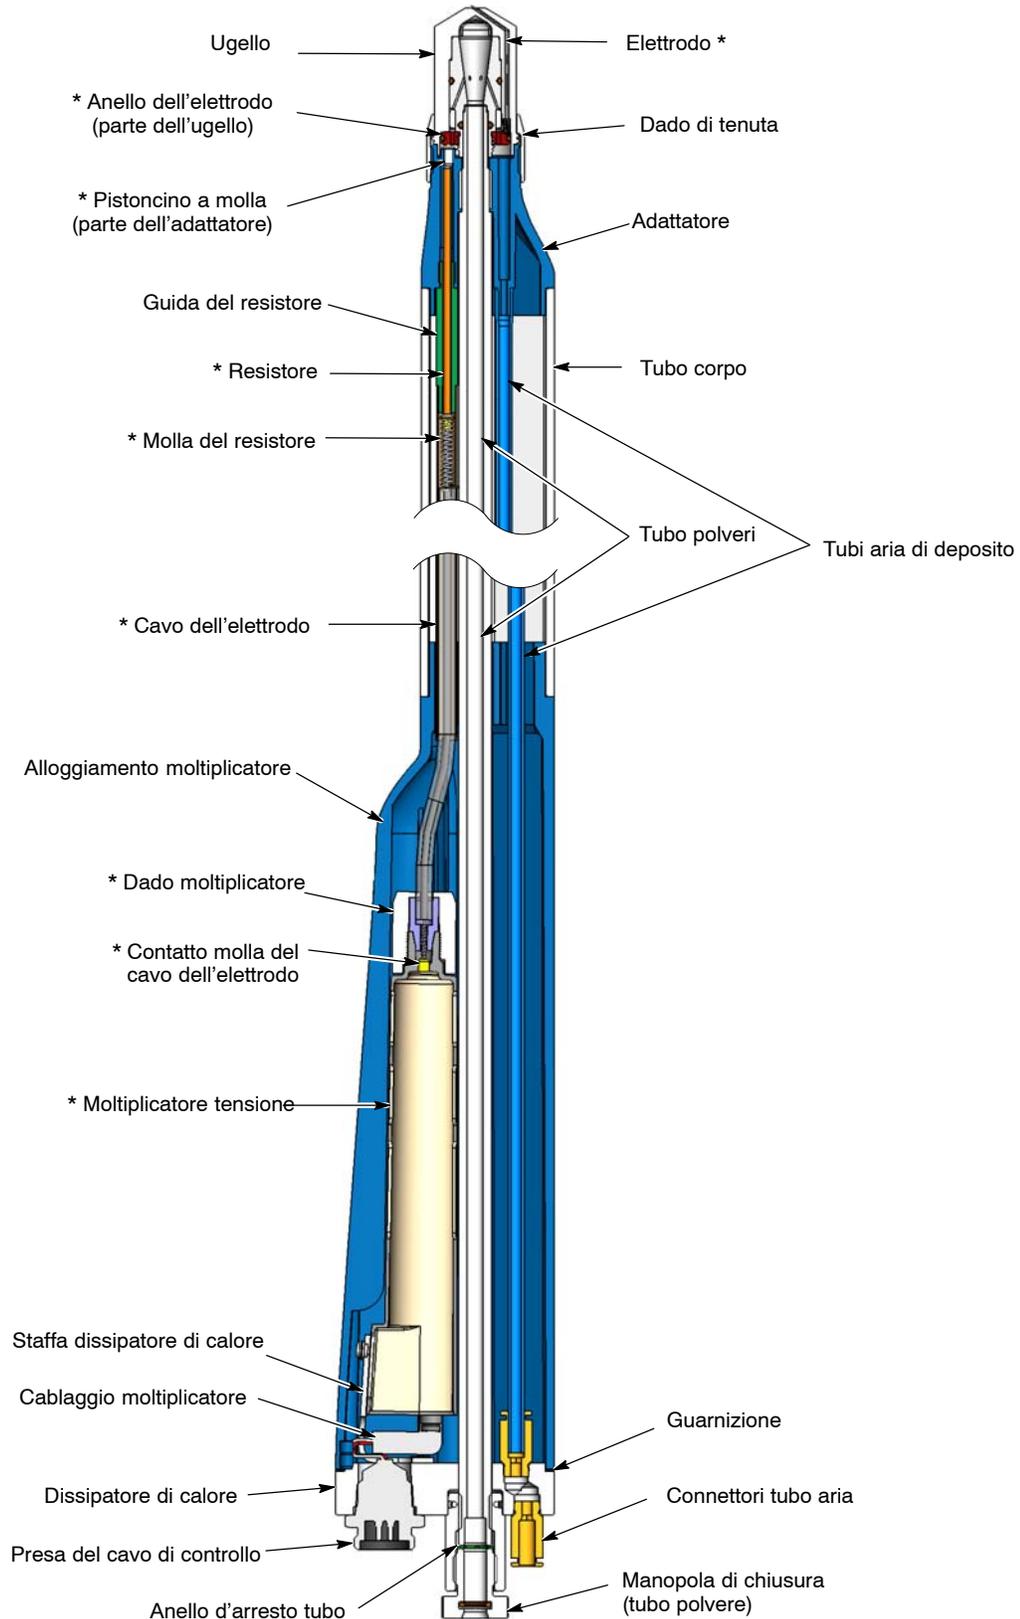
Immagine in sezione – Gruppo e componenti della pistola con montaggio su tubo
